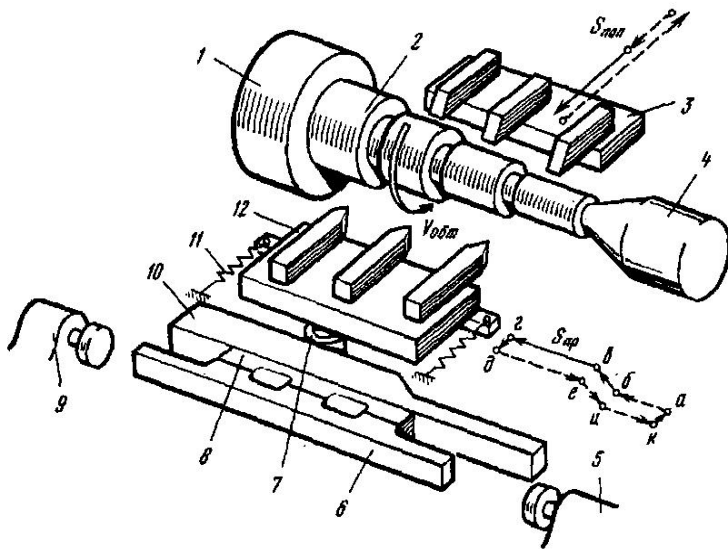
Схема роботи багаторізевого напівавтомата
